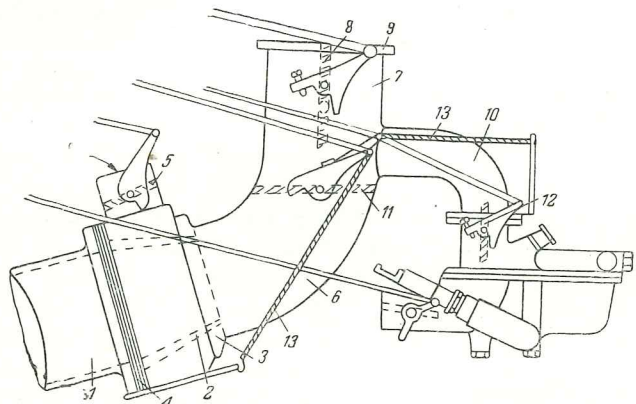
Схема смесителя газогенераторной установки Д-8а
